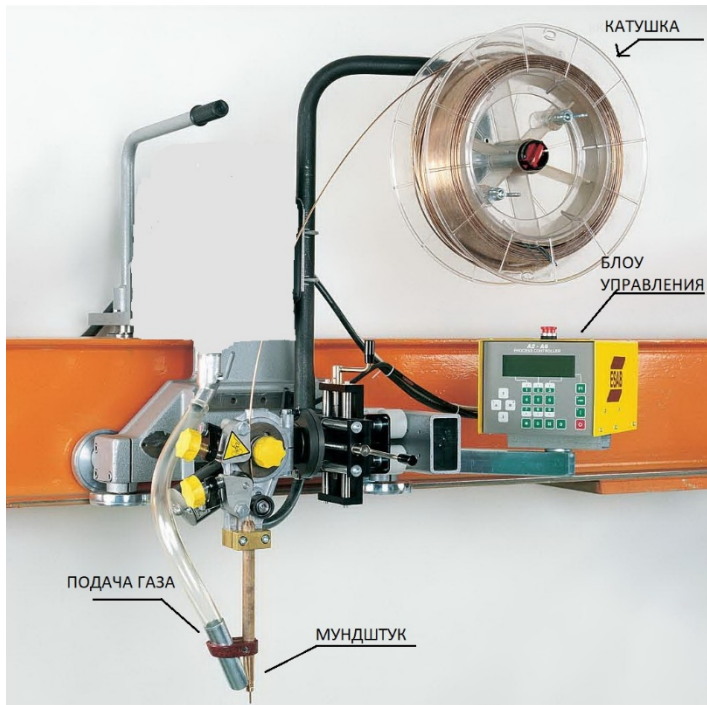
Сварочная головка TPRMS-22\44
